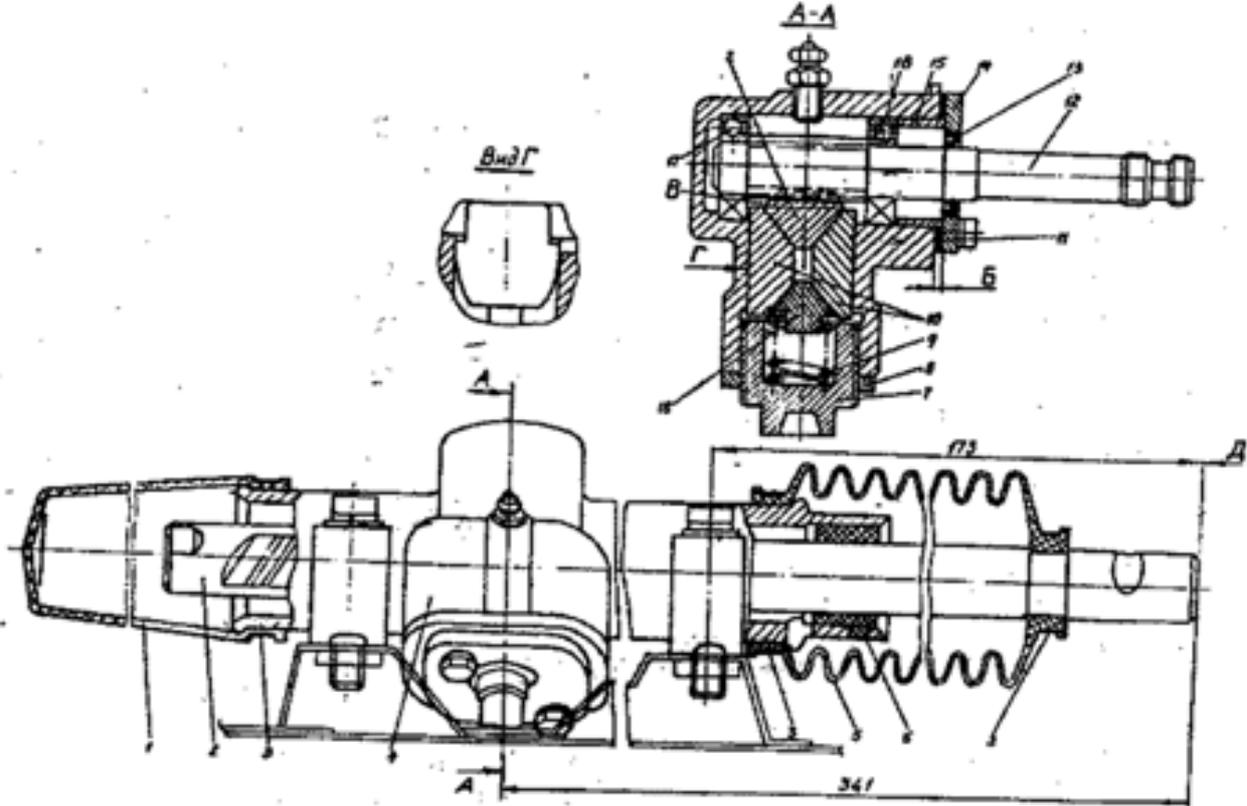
Механизм рулевого управления: 1 - чехол левый; 2 - рейка рулевого управления; 3 - хомут; 4 - картер; 5 - чехол правый; 6 - втулка рейки; 7 - пробка картера; 8 - гайка стопорная; 9 - пружина; 10 - упор рейки; 11 - прокладка регулировочная; 12 - шестерня; 13 - уплотнитель; 14 - крышка; 15 - втулка распорная; 16 - подшипник наружный; 17 - подшипник внутренний; 18 - подпятник; Д - положение рейки, соответствующее прямолинейному движению автомобиля; Б - величина для подбора компенсационных прокладок; В - полость для смазки.
